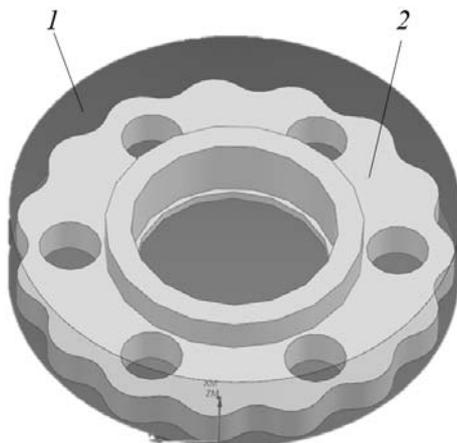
Результат фрезерования: 1 – цилиндрическая заготовка; 2 – сателлит
